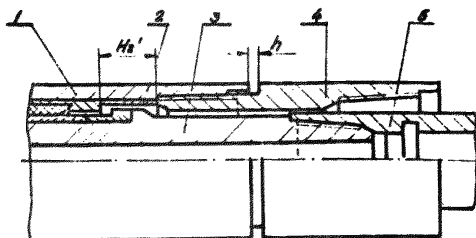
Определение высоты кольца корпуса: 1 - корпус; 2 - кольцо; 3 - вал; 4 - переводник; 5 - муфта шлицевая верхняя.
